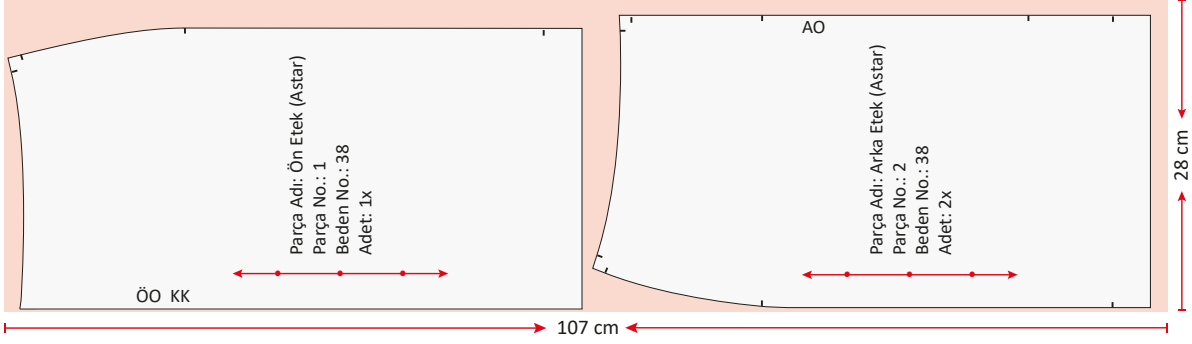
Çift en kumaşta hazırlanmış etek pastal planı
